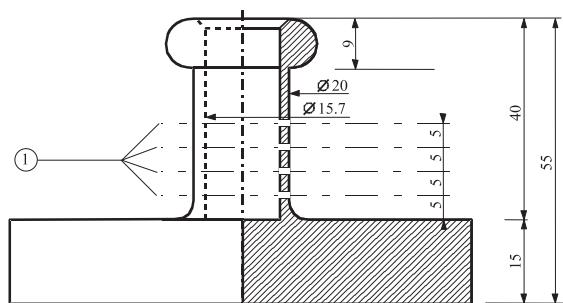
Полый бронзовый цилиндр, закрытый с одной стороны; чертеж и размеры детали в мм
